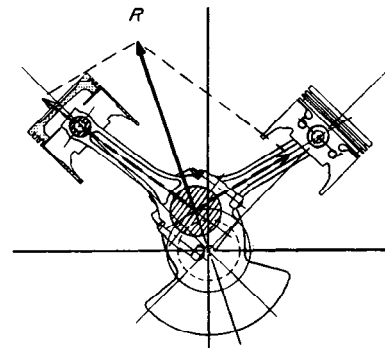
Resultante de las fuerzas de inercia y centrífuga debidas al movimiento rotativo y alternativo del cigüeñal y conjunto pistón-biela (Oldsmobile Division of General Motors Corporation).
